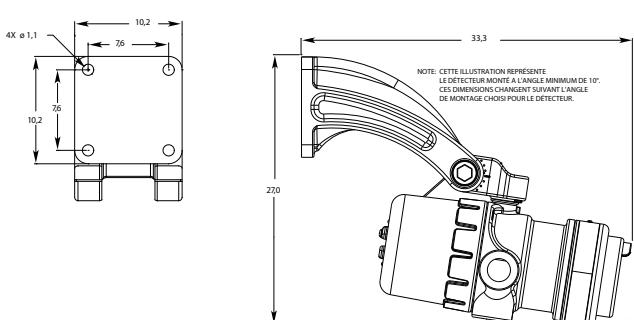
Dimensions du Support de Montage à Rotule Q9033 sans Collier de Fixation (cm)
